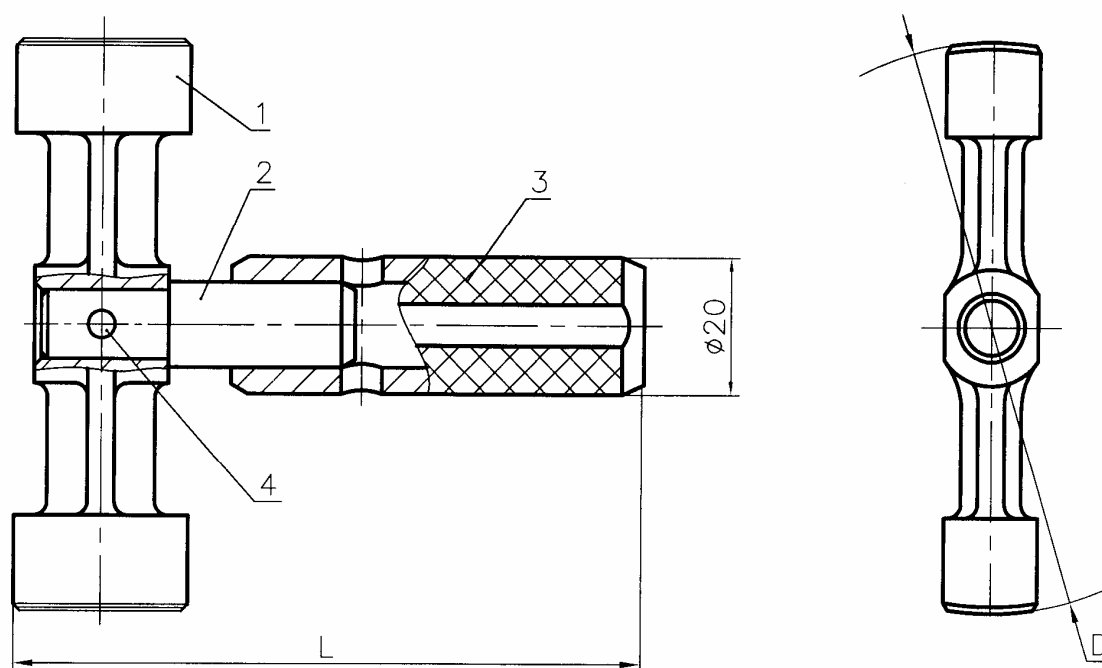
Гладкий штампованный неполный калибр-пробка:
